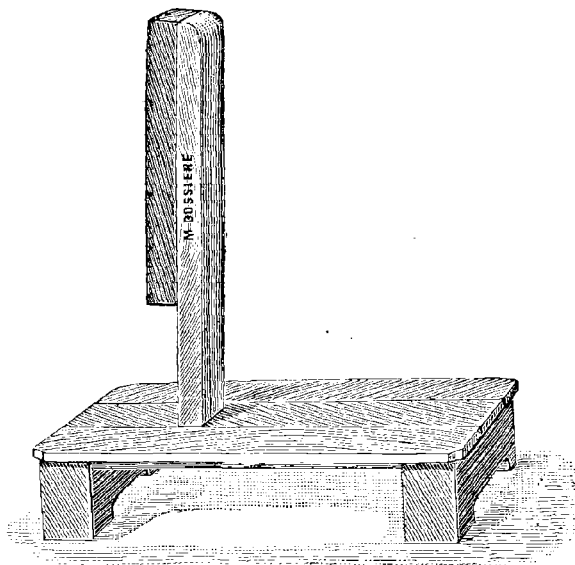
Chevalet anglais ordinaire pour le gros cuir surtout, sur lequel on *déraye* avec le couteau de corroyeur. Se compose essentiellement d'une planche de gaiac sur laquelle se fait le travail, celle-ci montée sur un montant en chêne fixé sur un plancher.
